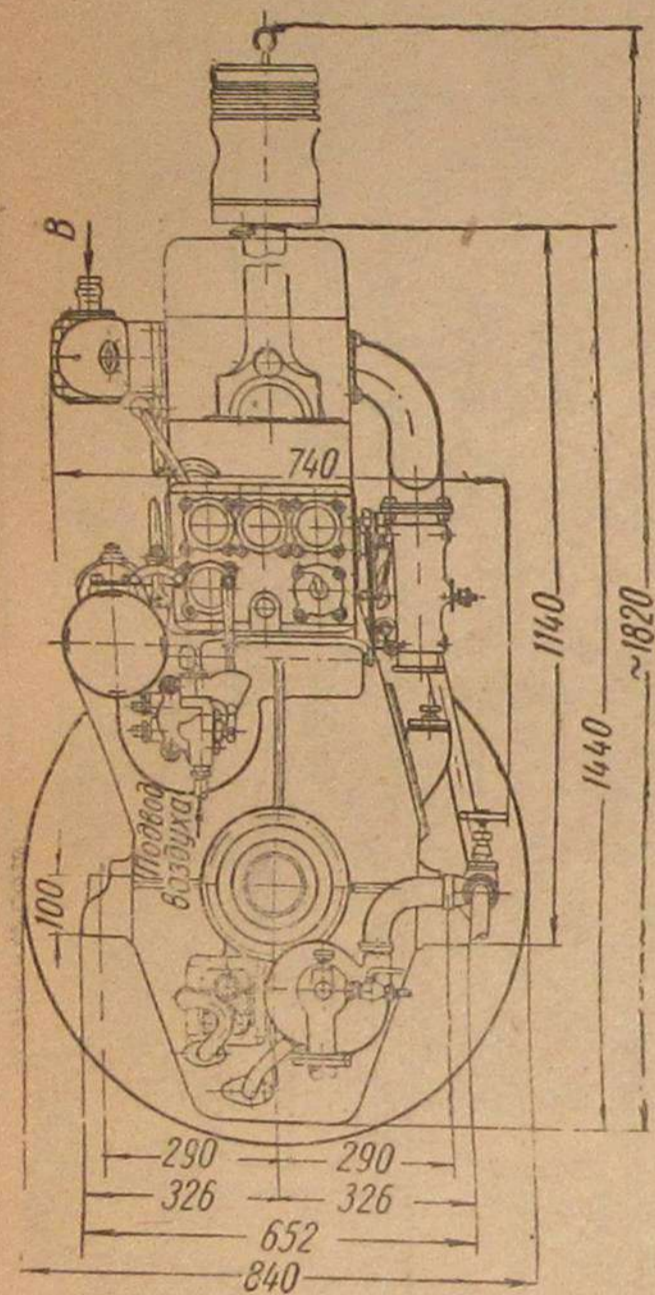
Газовый двигатель конструкции НИДИ 2ГЧ 18/26.
